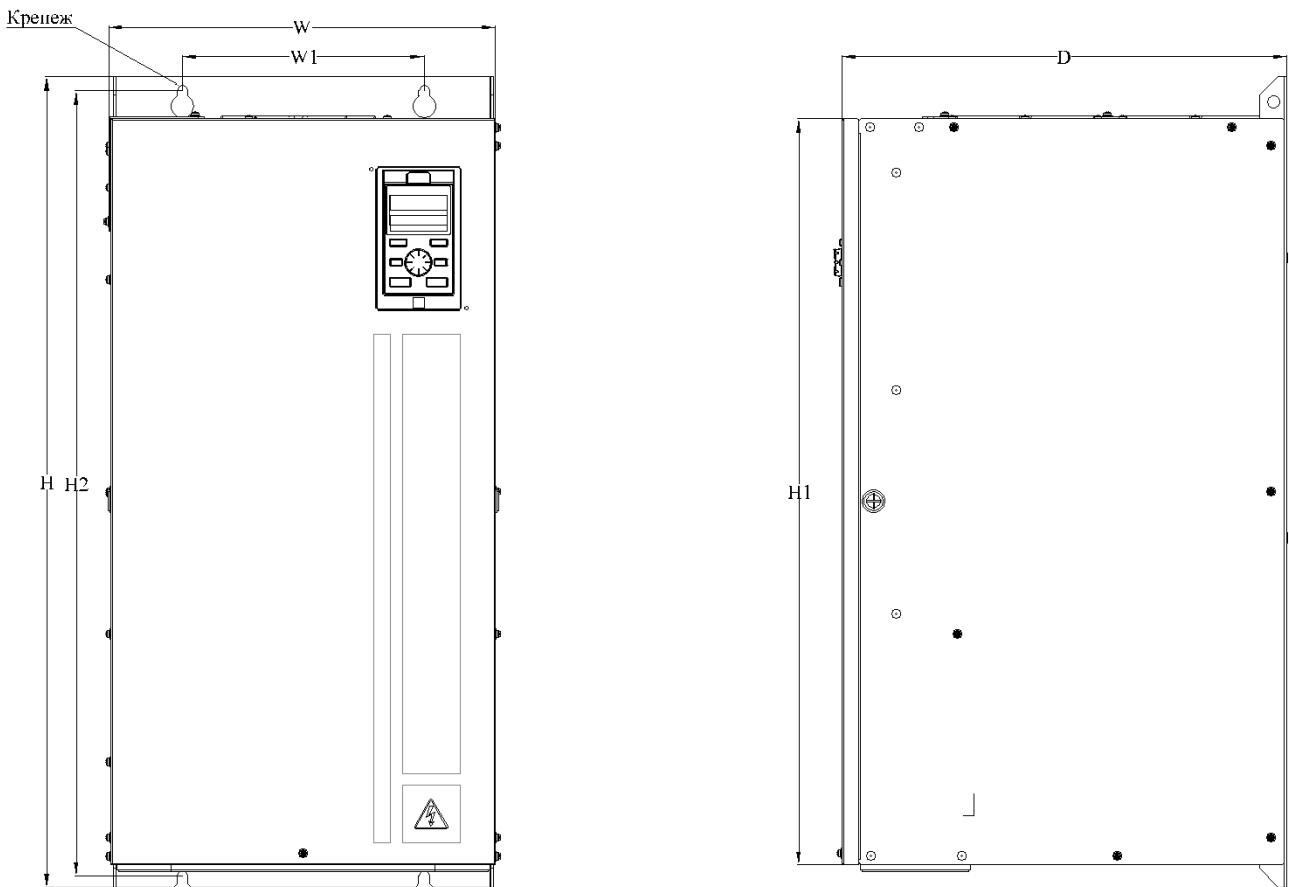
Чертеж преобразователя частоты типоразмер 7
